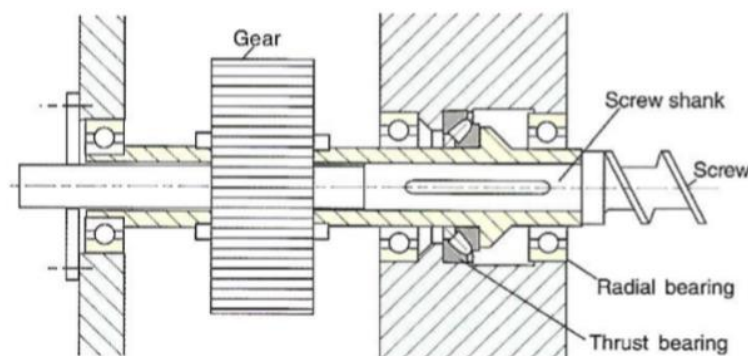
21 Ejemplo de un conjunto de cojinetes de empuje
